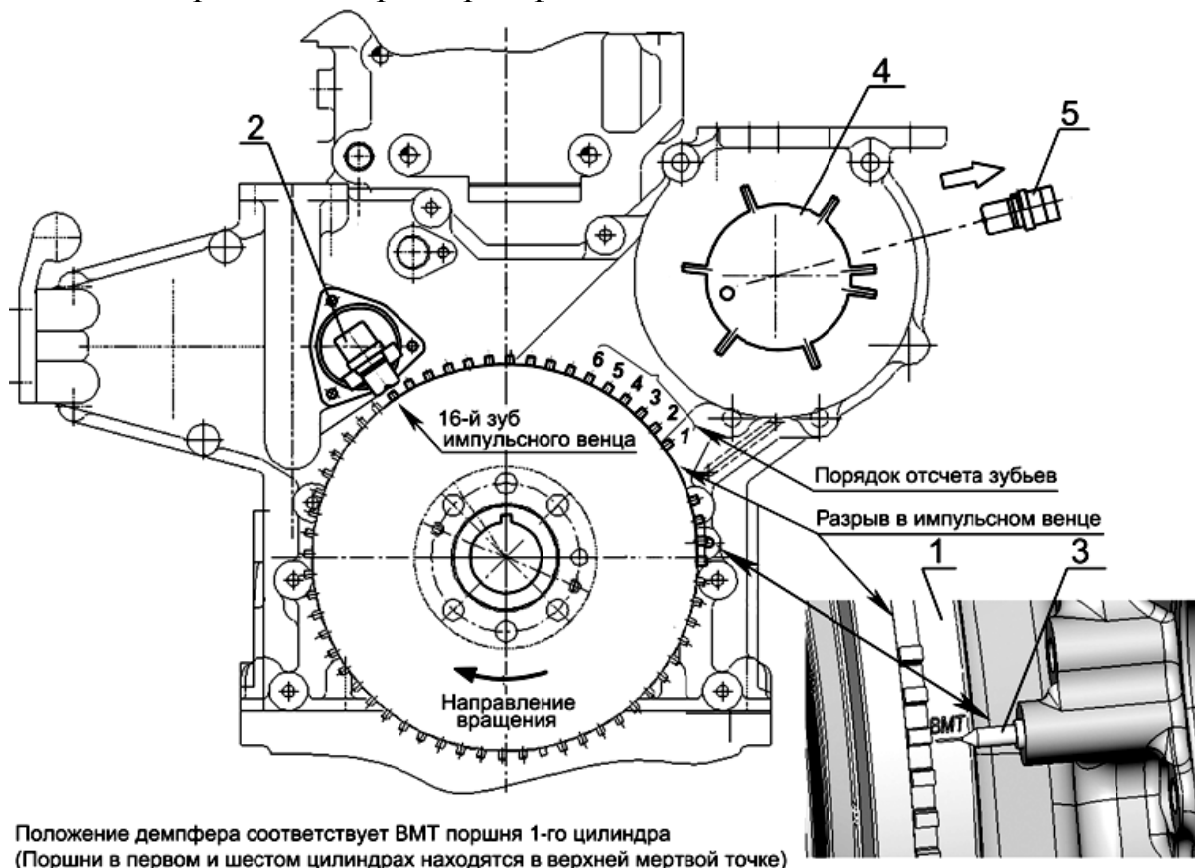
Приспособление для фиксации импульсного венца шестерни привода топливоподкачивающего насоса.
